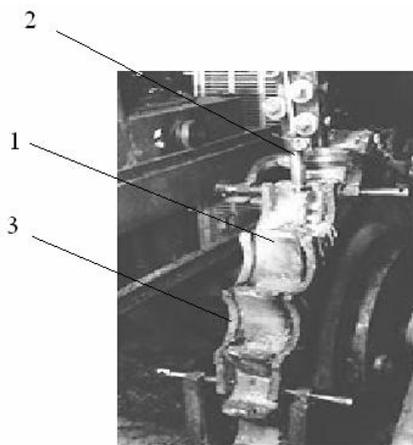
Наплавка ведущей звездочки бульдозера:
